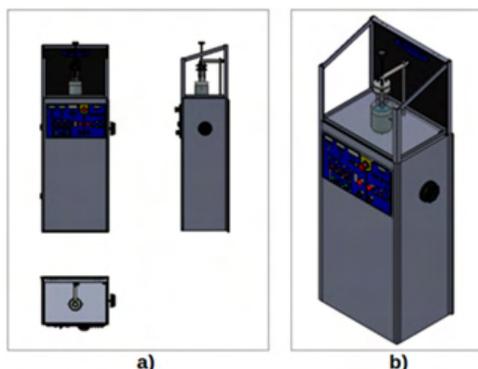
a) Vista do reator PEO montado b) Vista isométrica do reator montado.
